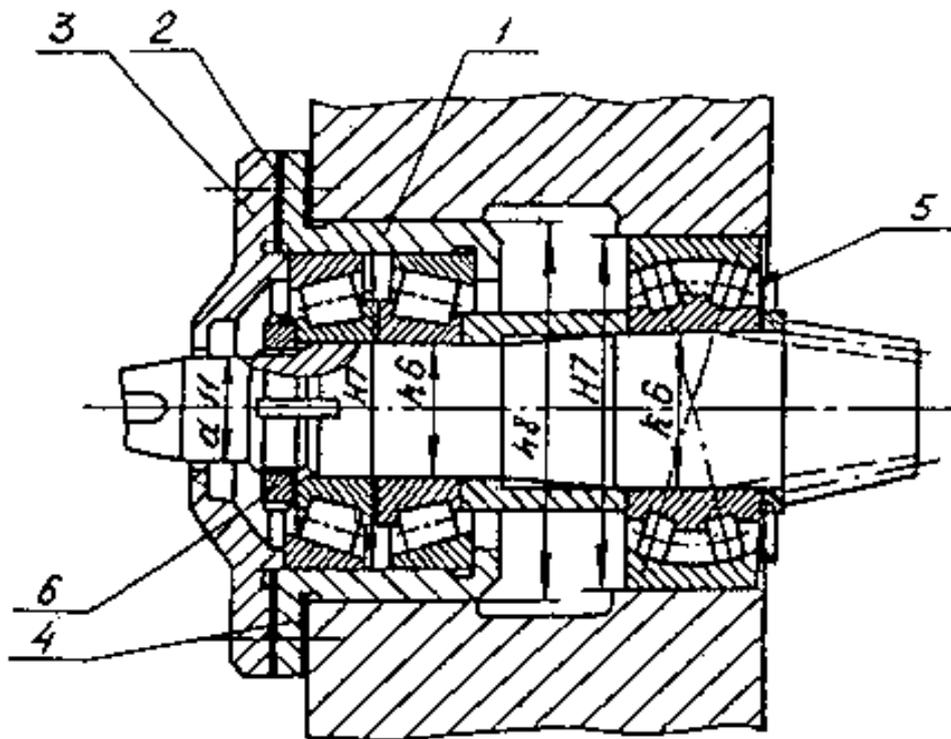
Пример конструкции подшипникового узла конической шестерни
